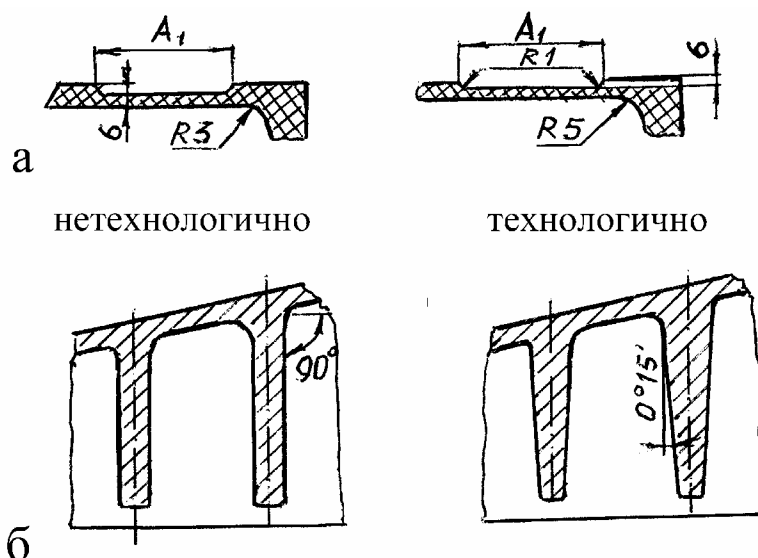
Конструктивное оформление деталей, изготовленных методом прессования : а – конструкция днища; б – конструкция узла крыла
